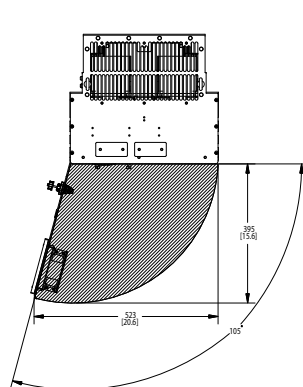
Пространство перед корпусом типа IP21/IP54, типоразмеры D2h, D7h и D8h.
